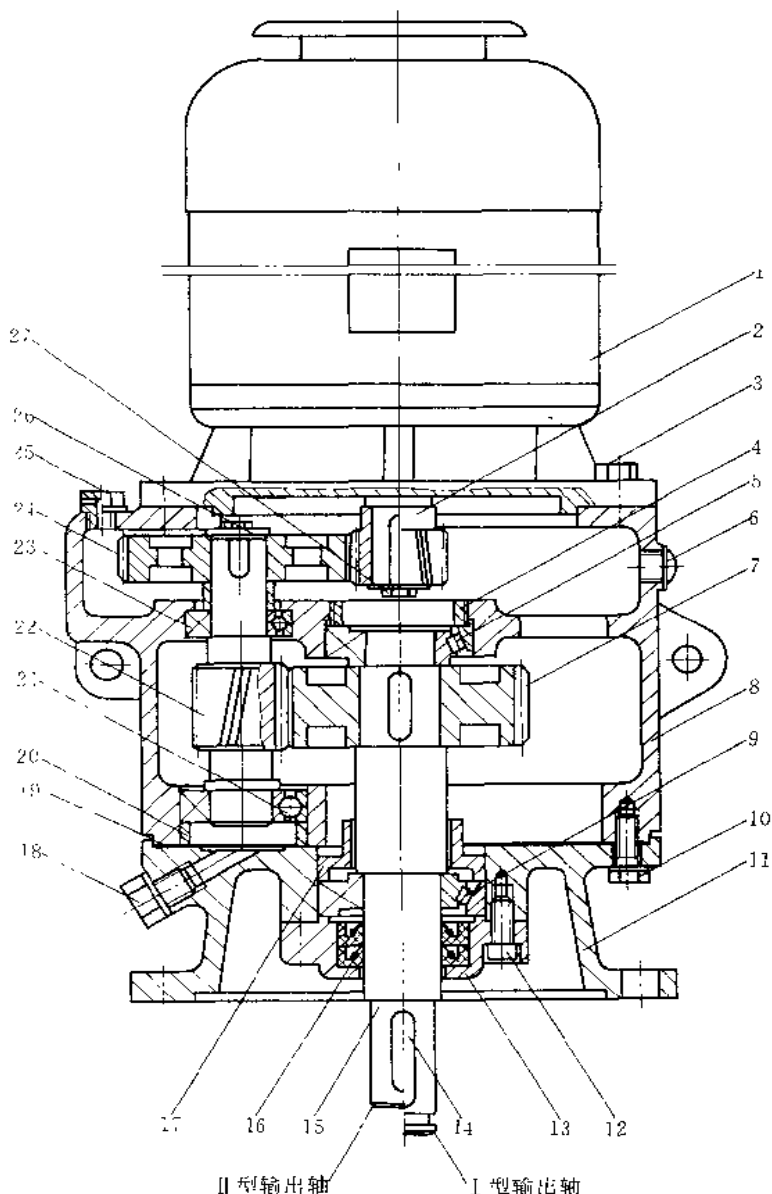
LC 型立式两级圆柱齿轮减速器
